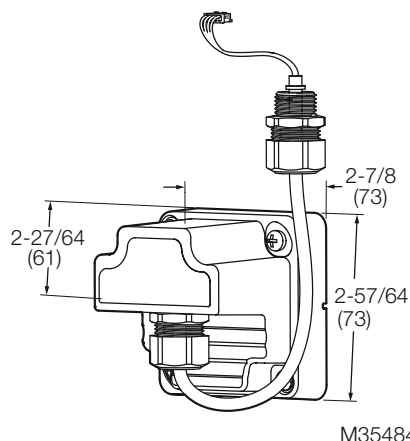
Dimensiones del módulo de presión en pulgadas (mm).
